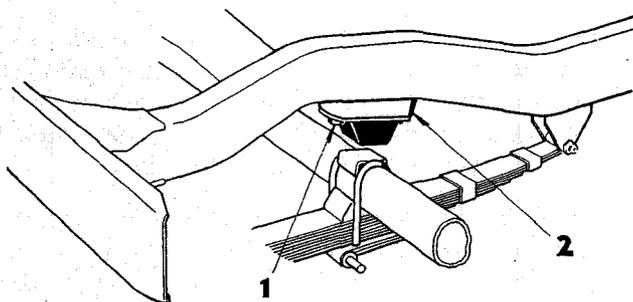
Zwischenblöcke für vord. Gumpuffer
